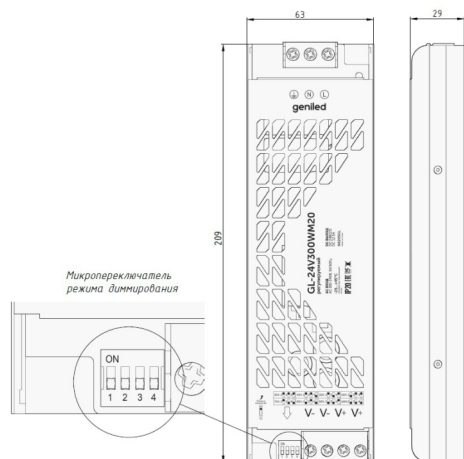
б. Габаритные размеры блока питания Geniled GL-24V300WM20 регулируемый
